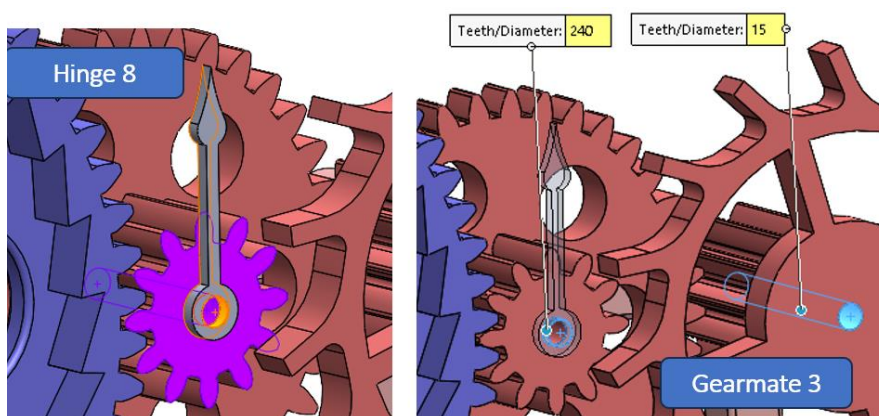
Constrangimento de Dobradiça 8 – Constrangimento Mecânico de Engrenagem 3
